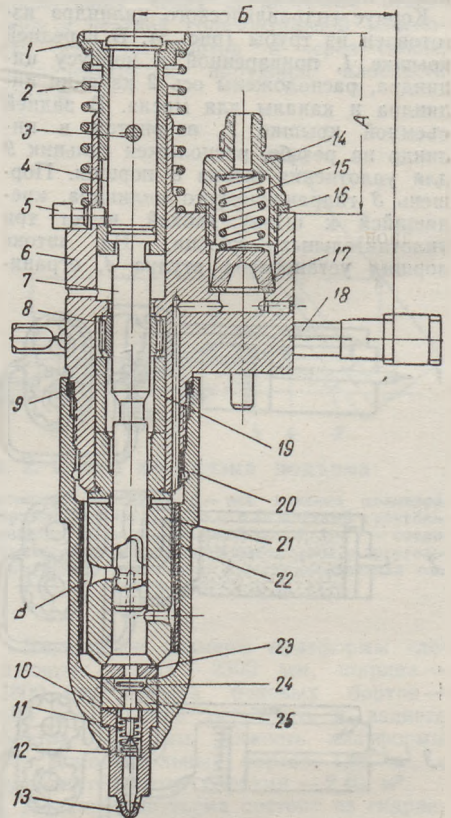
Насос-форсунка в разрезе: 1 — толкатель; 2 — пружина толкателя; 3 — штифт толкателя; 4 — стержень толкателя; 5 — стопор толкателя; 6 — корпус форсунки; 7 — плунжер; 8 — шестерня; 9 — прокладка стяжной гайки; 10 — основной обратный клапан; 11 — пружина обратного клапана; 12 — упор обратного клапана; 13 — распылитель (сопло); 14 — штуцер; 15 — пружина фильтра; 16 — прокладка штуцера; 17 — фильтр; 18 — рейка форсунок; 19 — дистанционная втулка; 20 — гайка стяжная; 21 — втулка плунжера; 22 — отражатель; 23 — седло пластинчатого обратного клапана; 24 — пластинчатый обратный клапан; 25 — седло основного обратного клапана.
